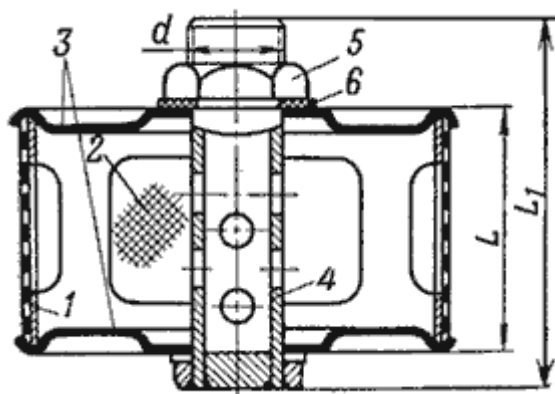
Сетчатый фильтр: 1 - корпус; 2 - сетка; 3 - диски; 4 - перфорированная трубка; 5 - гайка; 6 - прокладки.
